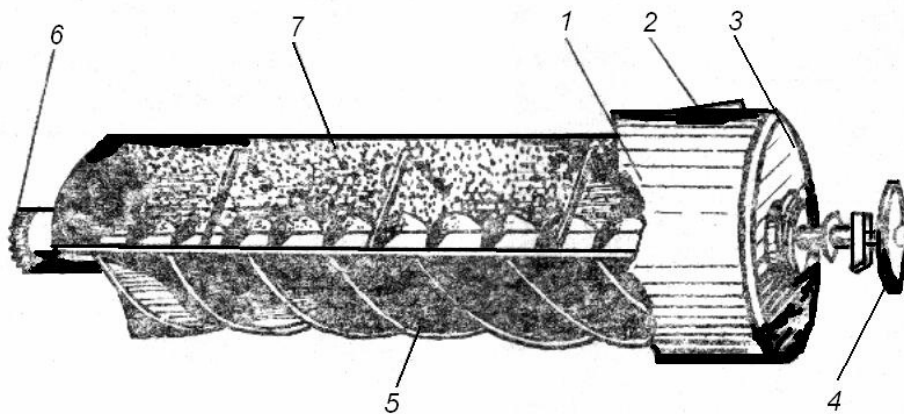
Триерный цилиндр: 1 – обечайка; 2 – стяжка; 3 – розетка;
